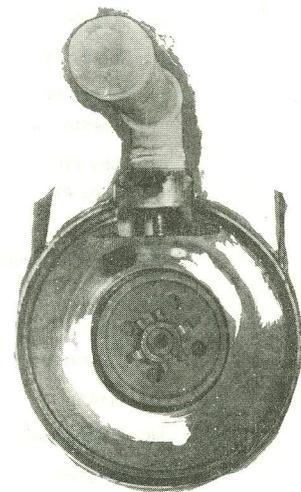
Detalhe da montagem do dispositivo à base da plantadeira.
